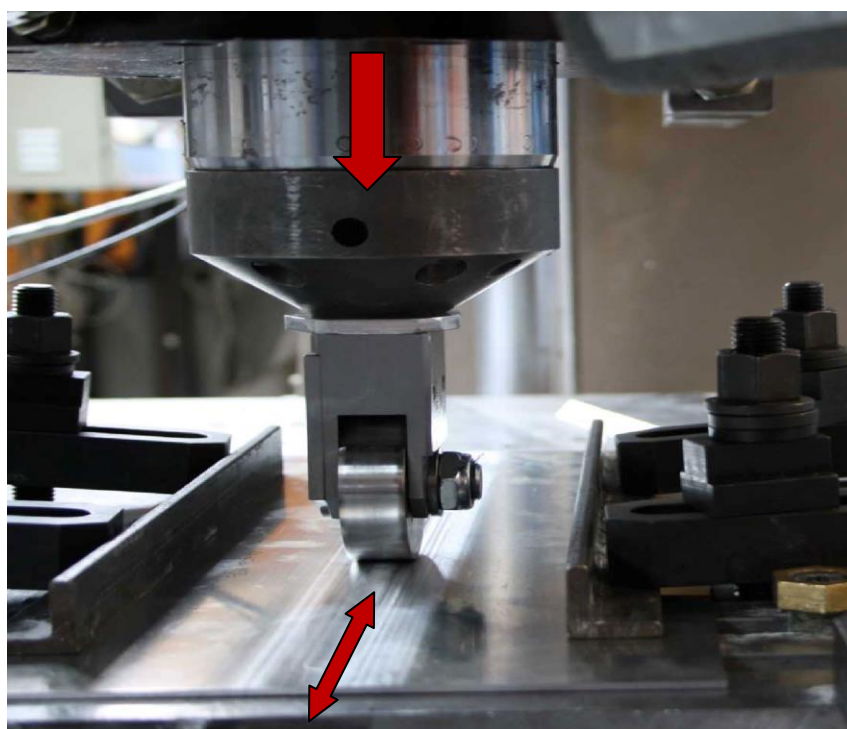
Rouleau de galetage sur une plaque soudée.
